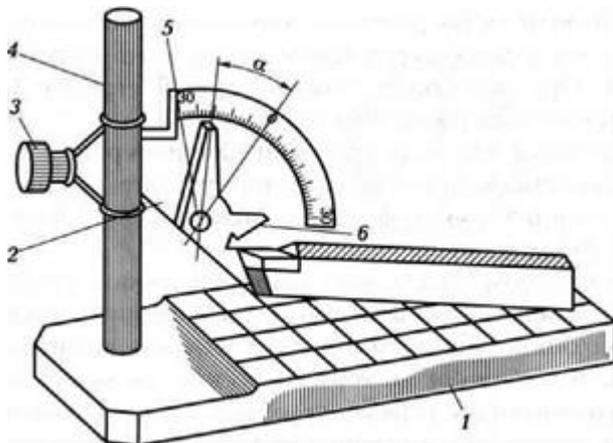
Настольный угломер конструкции МИЗ: 7 — плита (основание); 2 — шкальное устройство; 3 — фиксатор; 4 — стойка; 5 — винт; 6 — измерительная линейка
